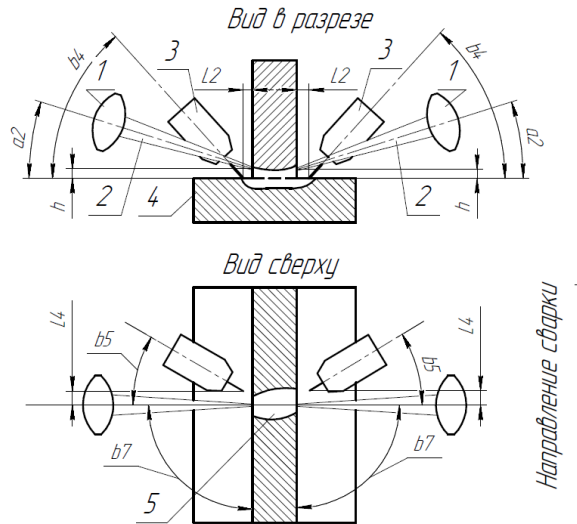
Схема ГЛДС, метод «Гибрид Тандем» стыкового сварного соединения в нижнем положении (РА):
